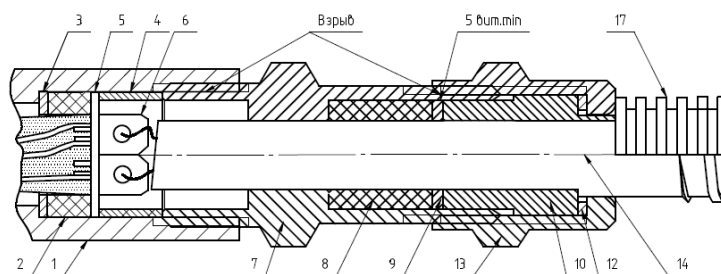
Конструкция исполнительного блока ИО102-58 Рис.3 Габаритные и установочные размеры задающего блока ИО102-58
